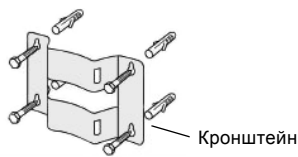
Пример монтажа на стену с использованием стенового кронштейна
